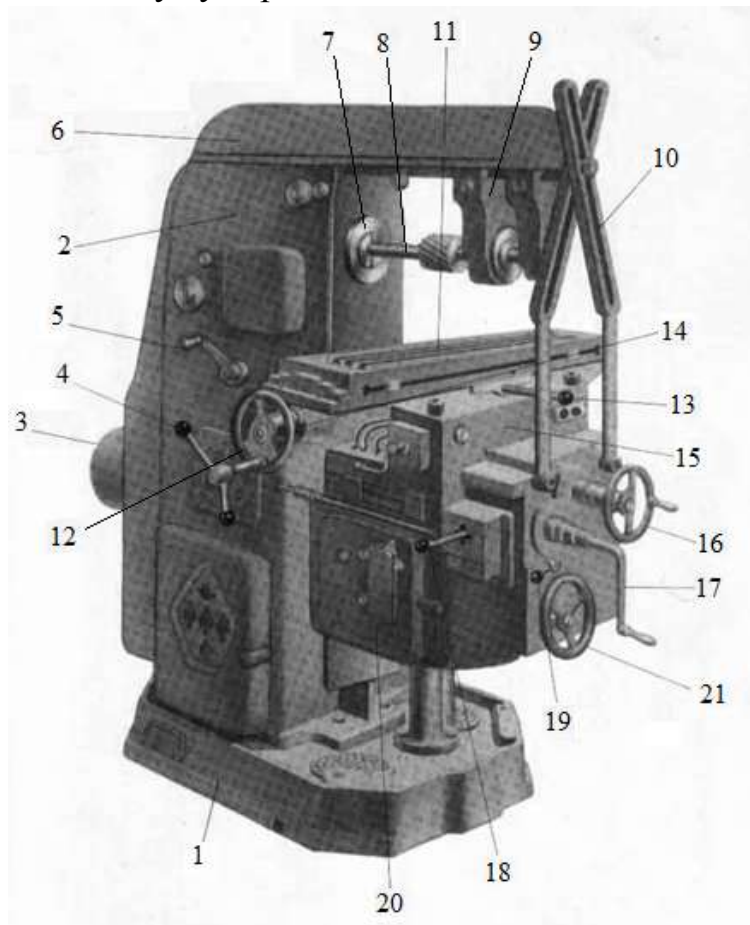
Загальний вид горизонтально-фрезерного верстату 6П80
